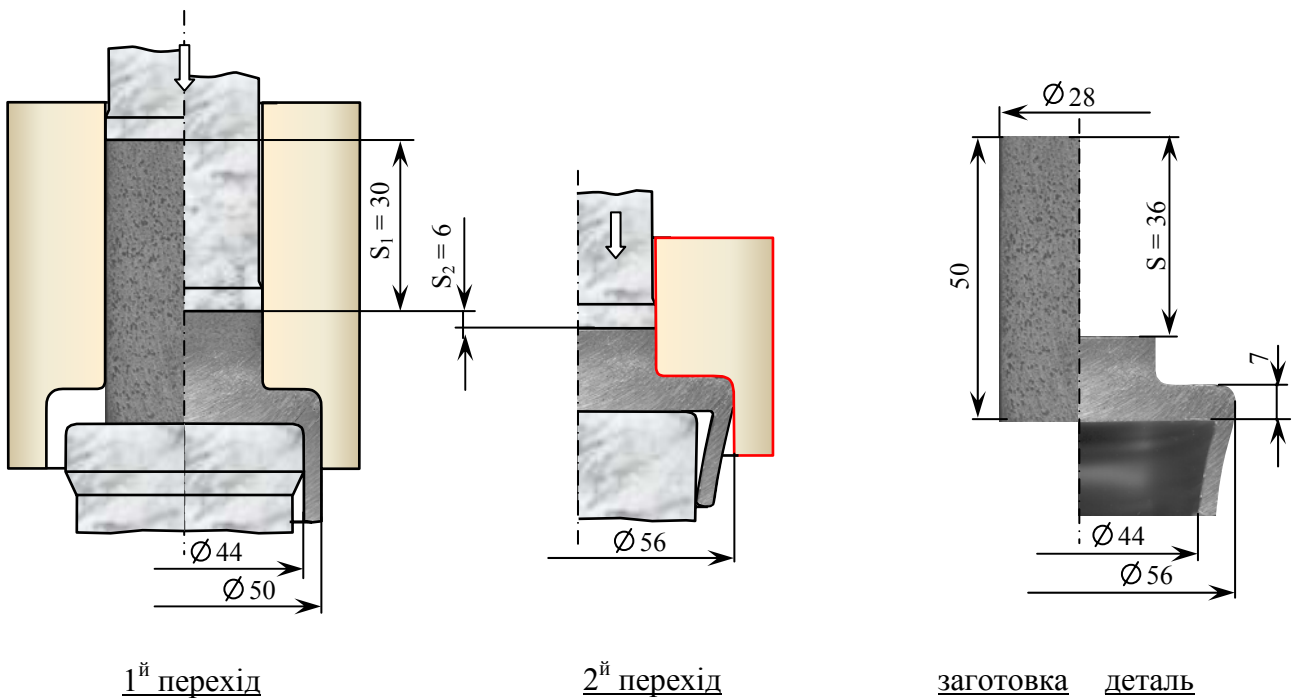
Виготовлення складнопрофільованого виробу типу стакану з кінчними зовнішньою та внутрішньою поверхнями за рахунок зміни розміру матриці
